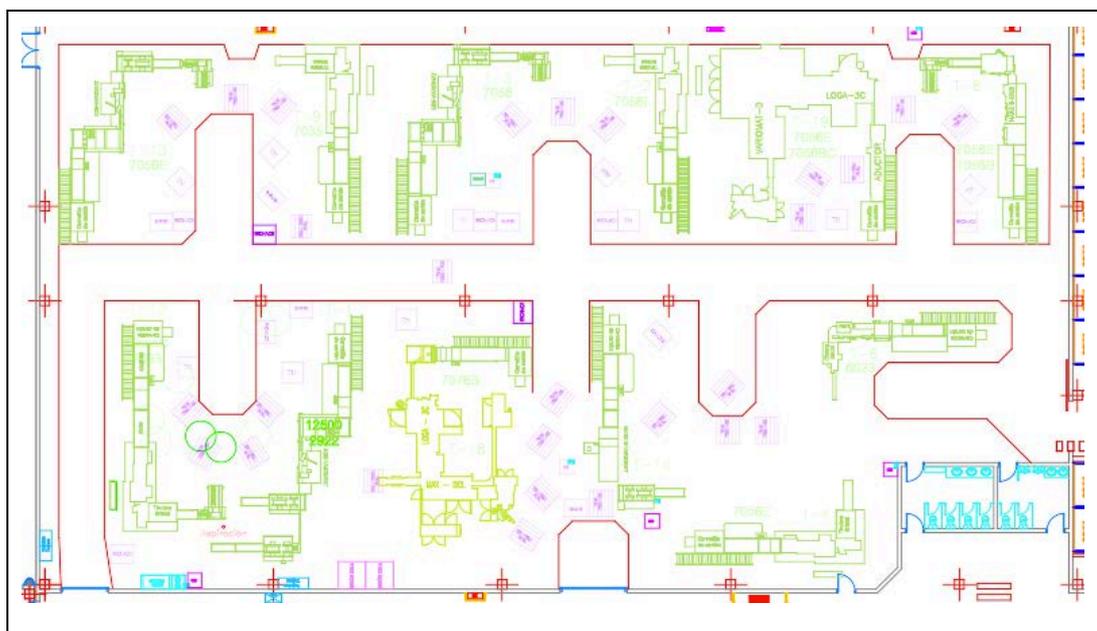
Plano detalle de las máquinas en la sala de tirulos. [Fuente: Elaboración propia]
